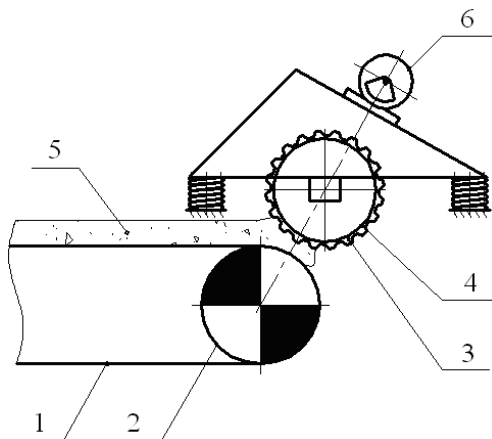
Подпрессовочный механизм: 1 – лента конвейера; 2 – разгрузочный барабан; 3 – рифленая поверхность; 4 – прессующий валок; 5 – слой шихты; 6 – вибровозбудитель
